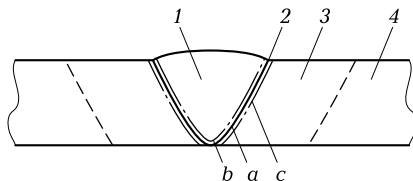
Схема поперечного сечения сварного соединения:
